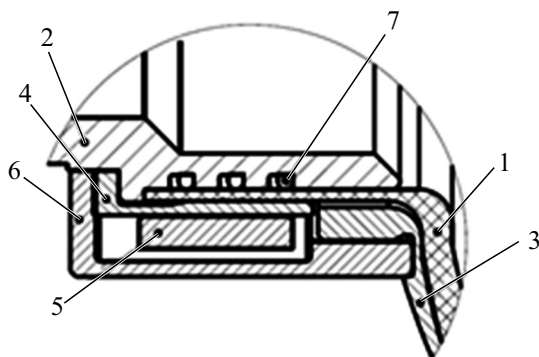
Конструкция заправочно-расходного узла: 1 — полимерный лайнер; 2 — втулка-ниппель; 3 — фланец; 4 — разрезная втулка; 5 — кольцо; 6 — крышка; 7 — уплотняющие манжеты.
